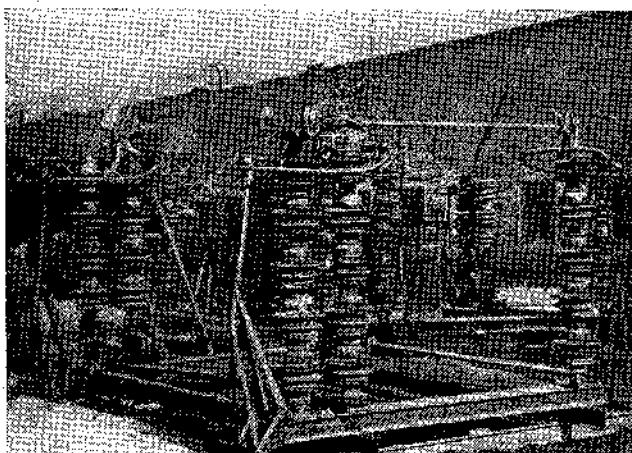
Сборка разъединителя 110 кв на МЗУ
